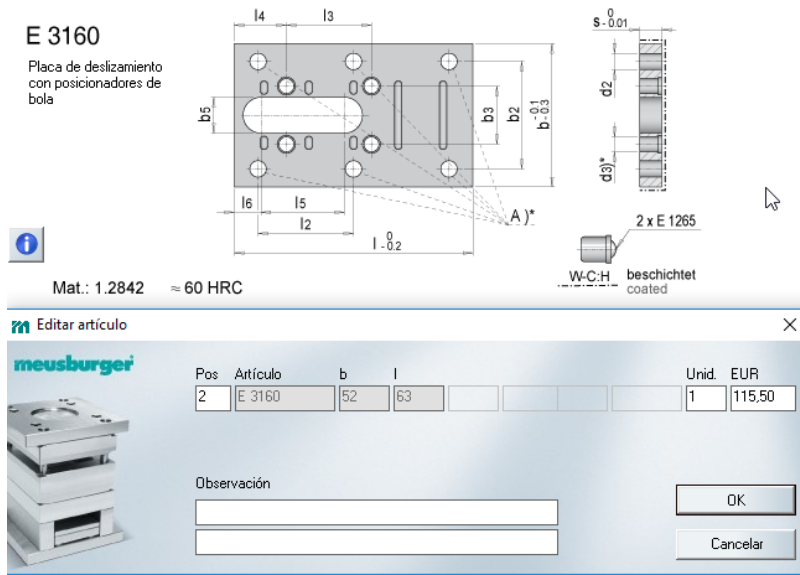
5.2 Placa de deslizamiento con posicionadores de bola.
